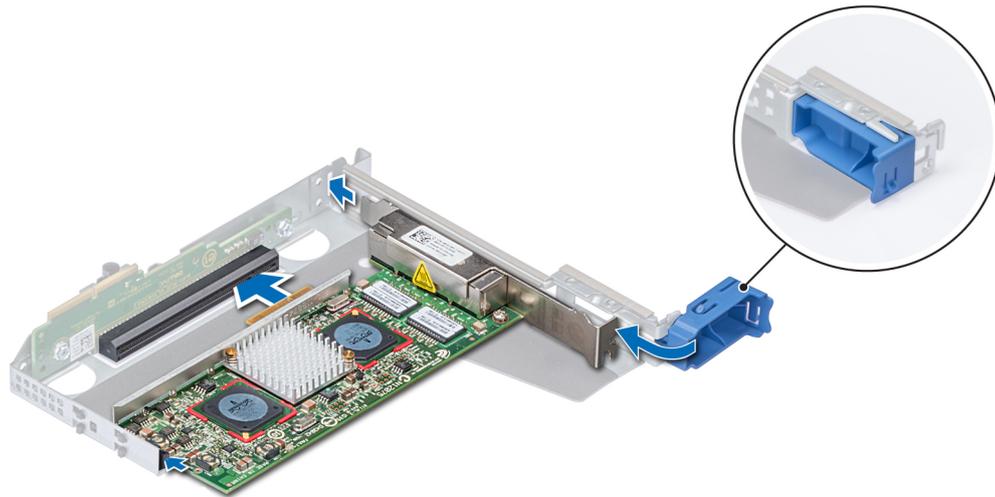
Installation d'une carte d'extension sur la carte de montage 1
